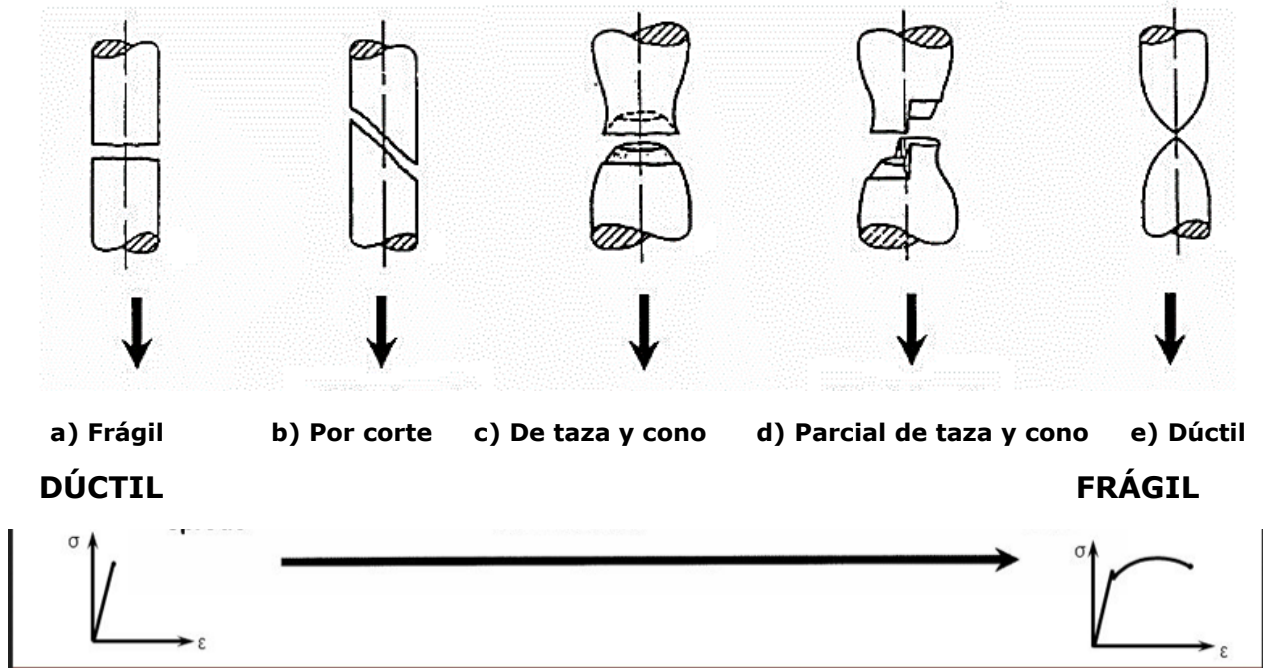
Tipos de fallas en elementos sometidos a tensión.
